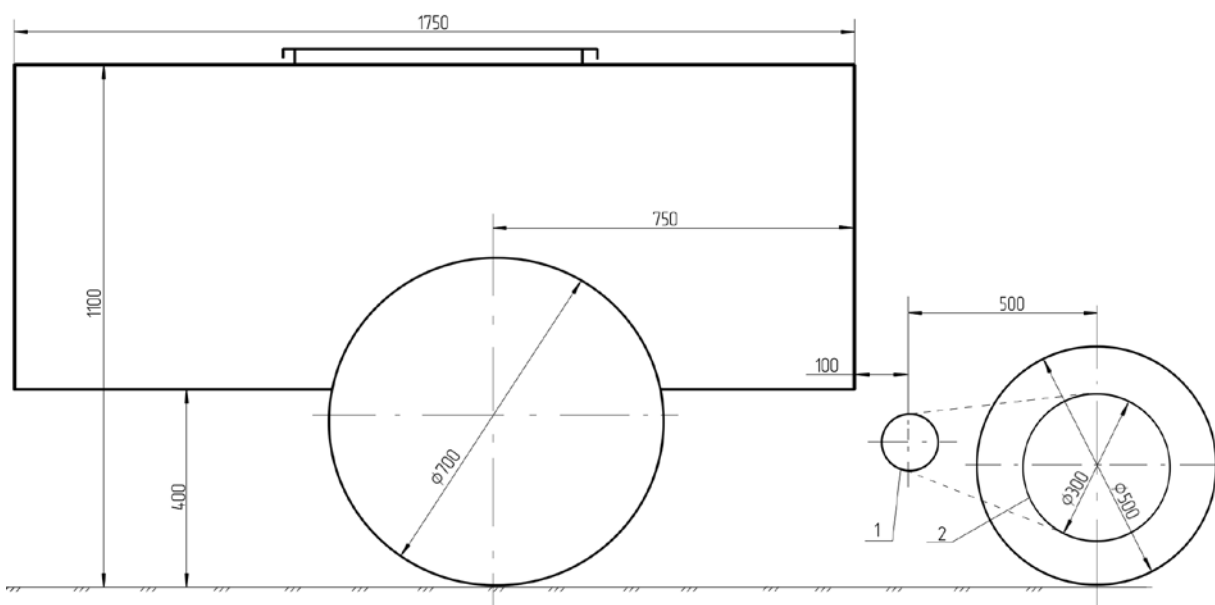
Схема компоновки индивидуального приводного колеса с приставным вариантом: 1 – звездочка ведомая; 2 – звездочка ведущая
